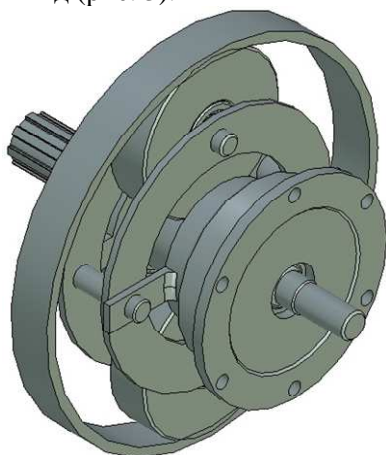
3D-модель уравновешенного двухсателлитного редуктора
